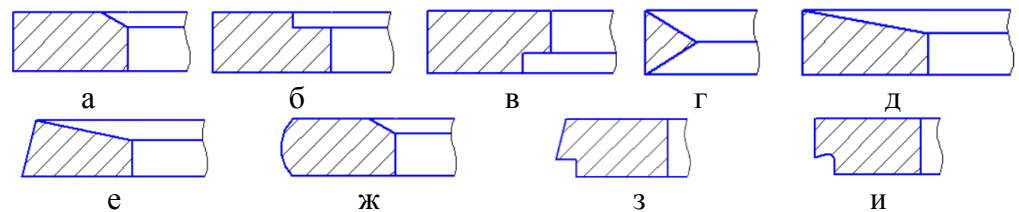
Профили поршневых колец: а – прямоугольный; б – с верхним внутренним углом; в – с нижним внутренним углом; г – треугольный; д – несимметричный трапециевидный; е – конический; ж – бочкообразный; з – конический скребковый; и – скребковый
